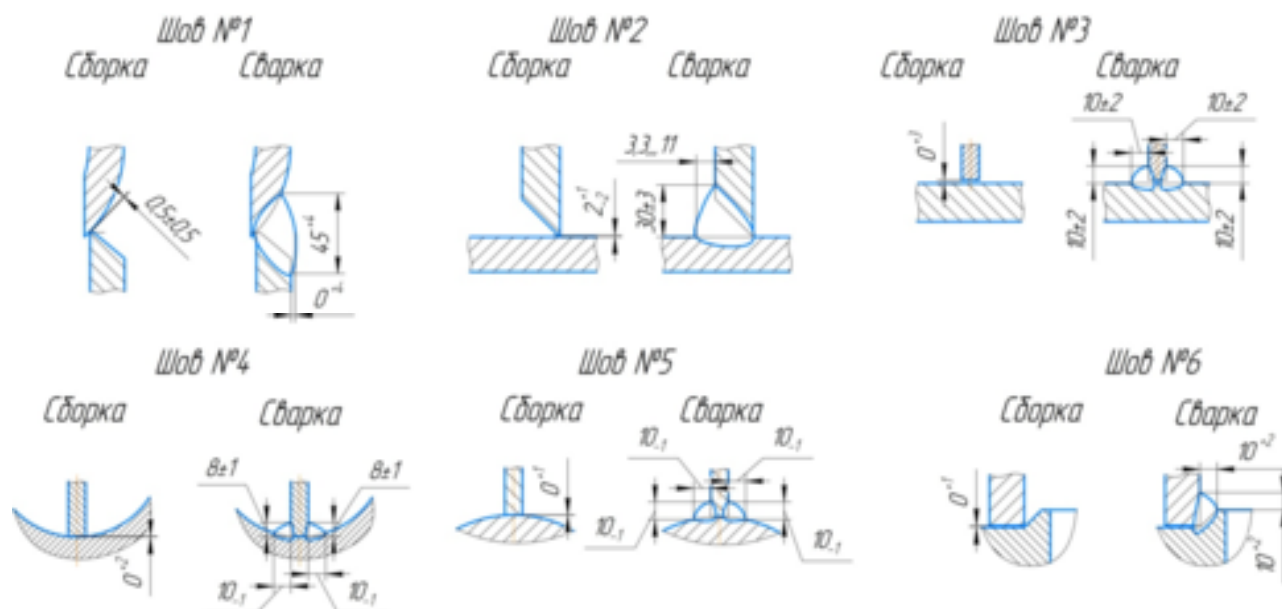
Параметры проверки ВИК швов при сборке и сварке
